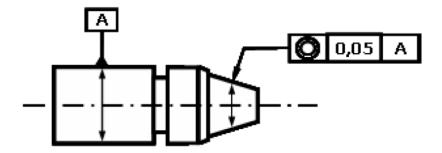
Indicação de tolerância de coaxialidade em desenho técnico
